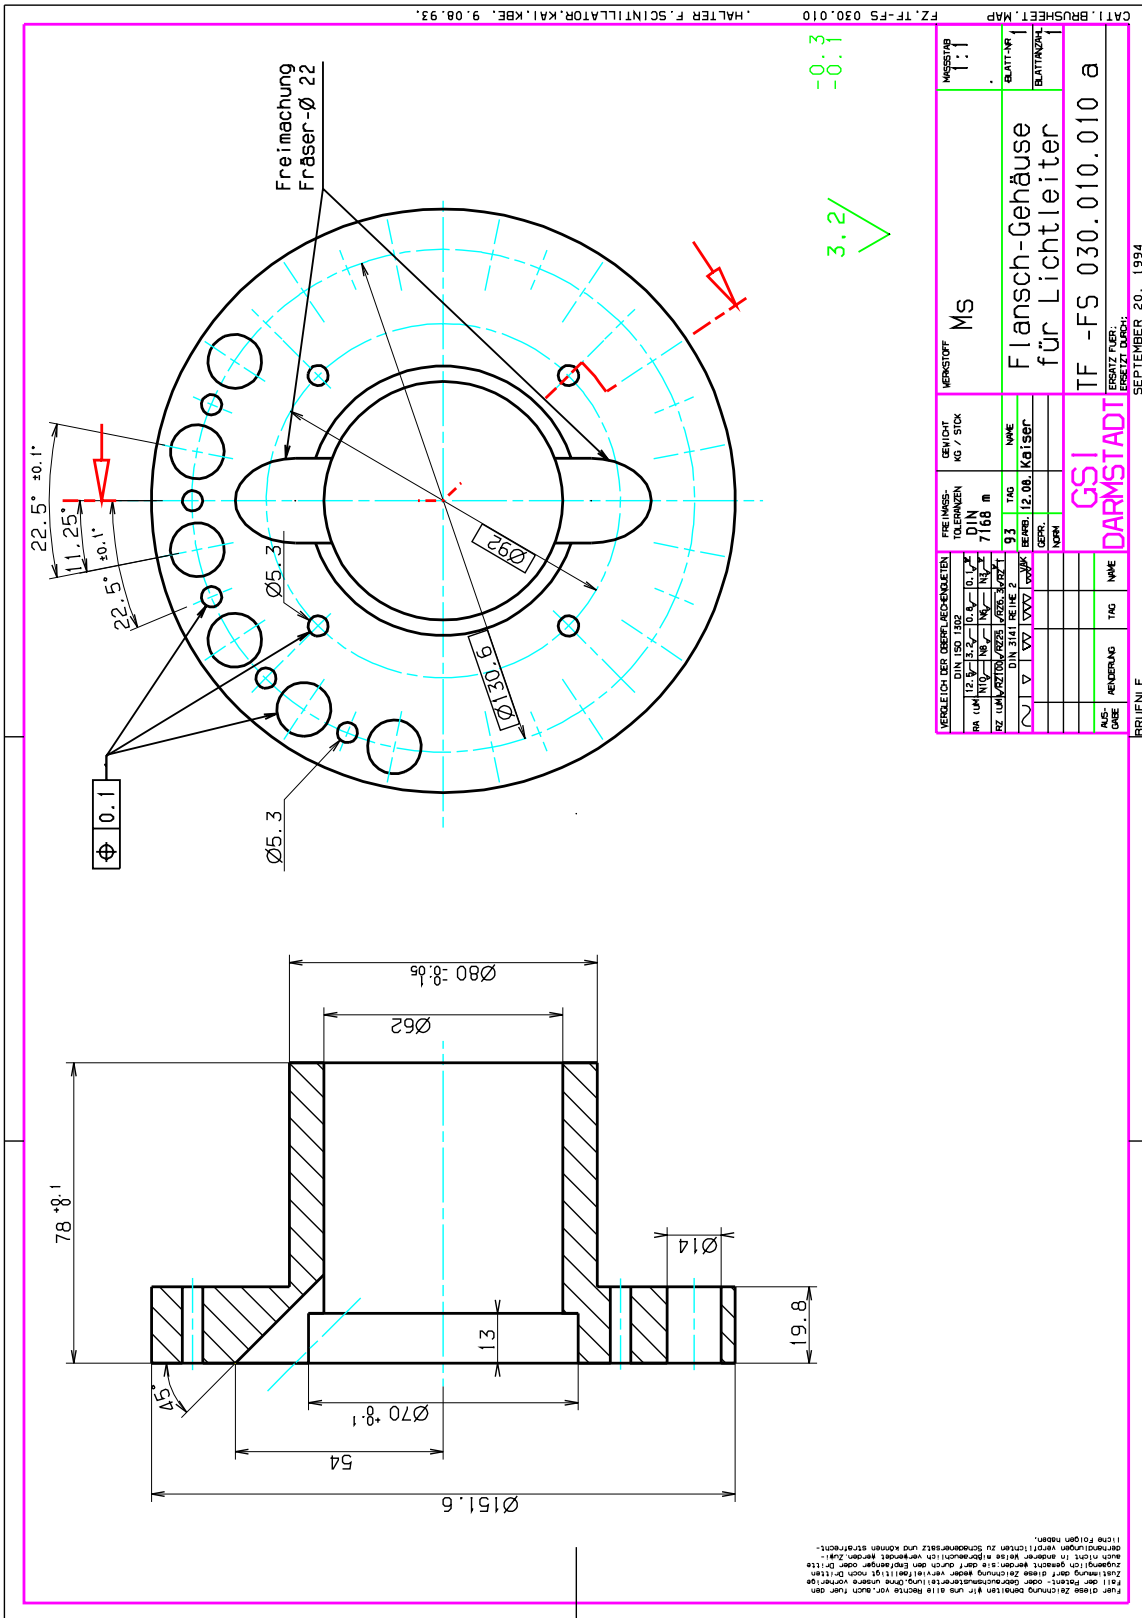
Vakuumtauglicher Szintillator: Flanschgehäuse für Lichtleiter.
